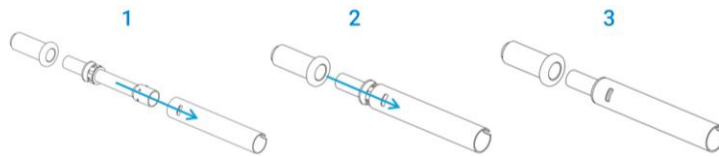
Vue illustrée présentant le remontage de l'ensemble de tubes externes en céramique
